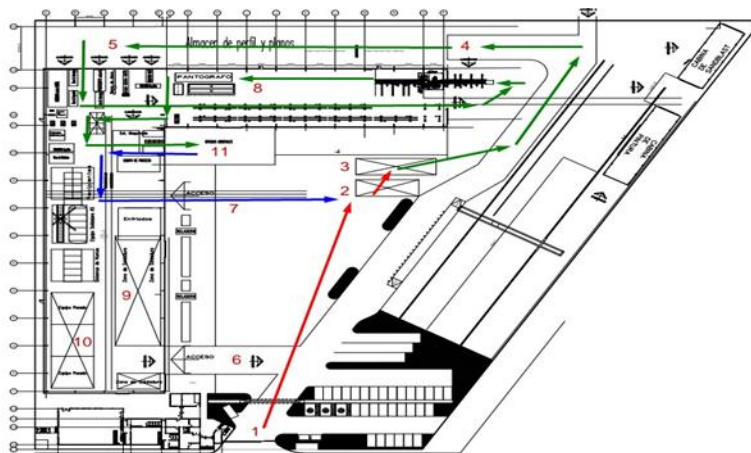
Layout mejorado 3 de la Planta Durosa Santa Rosa SA, de CV.
